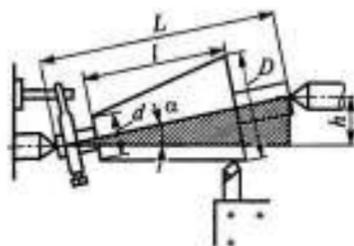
Обработка конической поверхности путем смещения задней бабки:
